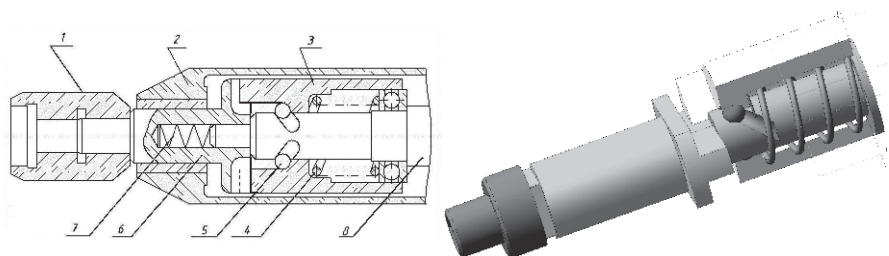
Ударно-вращательный механизм с винтовым движением ударника: 1 — ключ; 2 — корпус; 3 — ударник; 4 — рабочая пружина; 5 — шарико-винтовая пара; 6 — шпindelь-наковальня; 7 — возвратная пружина; 8 — приводной вал
